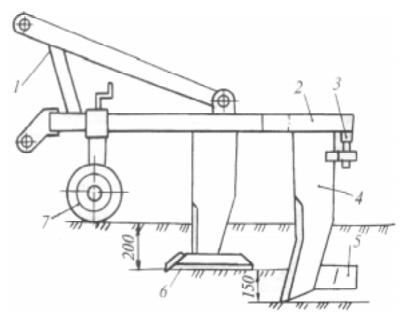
Комбинированный плоскорез-щелеватель: 1 — навеска; 2 — рама; 3 — упор; 4 — щелерез; 5 — уширитель щели; 6 — лапа; 7 — колесо
